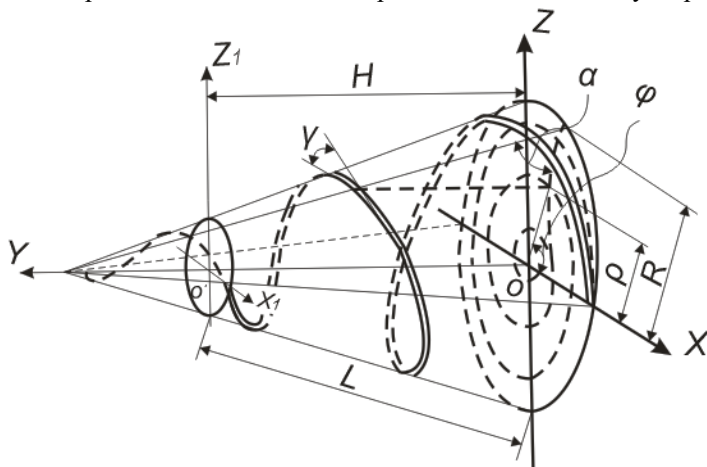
Схема для визначення довжини прутка, з якого виготовляється конічний валець
